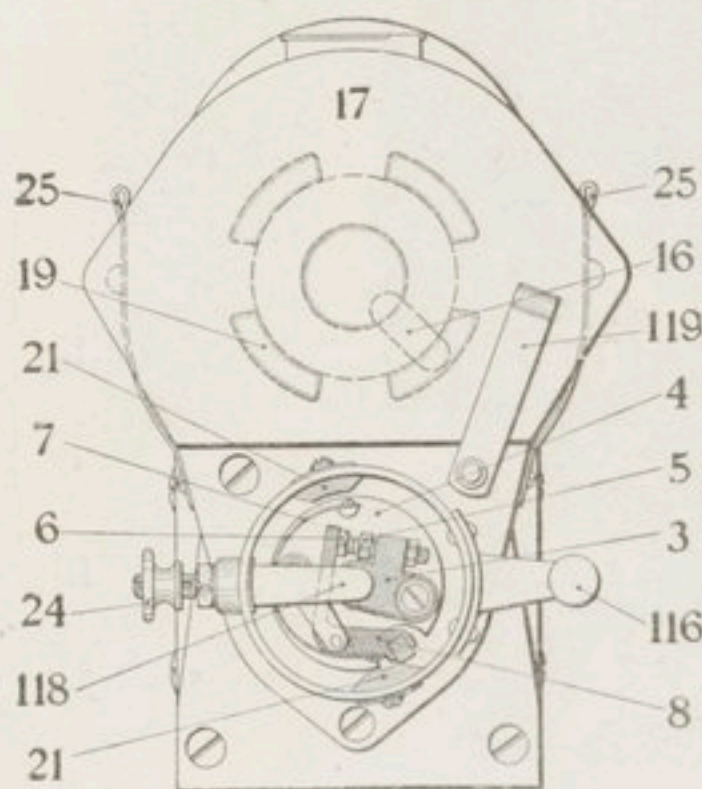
Magnéto Bosch pour moteur à quatre cylindres. Vue arrière.
